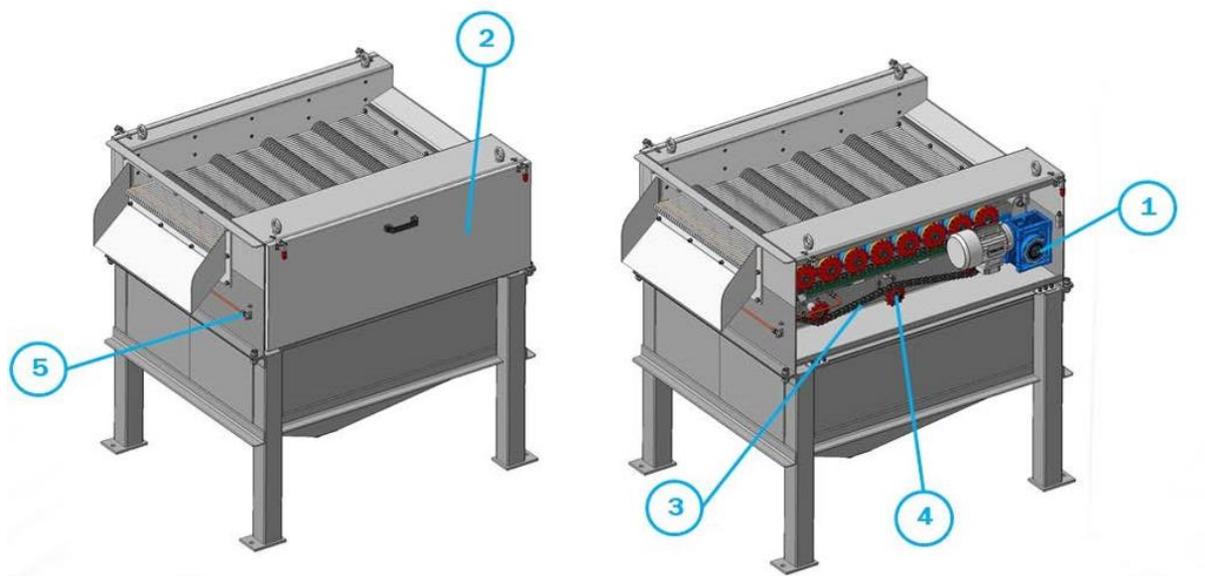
Техническое обслуживание волнового сепаратора: 1 – боковая крышка; 2 – червячный мотор-редуктор; 3 – цепная передача; 4 – натяжная звездочка; 5 – пресс-масленки.
